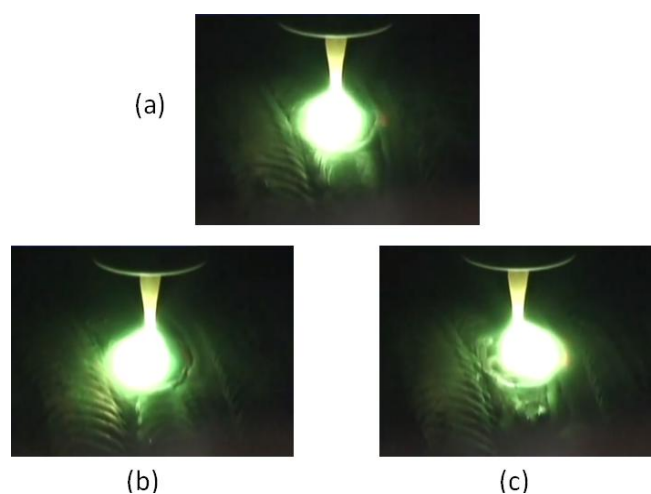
Soldagem GTAW autógena. (a) arco na posição central, (b) arco à esquerda, (c) arco à direita.
